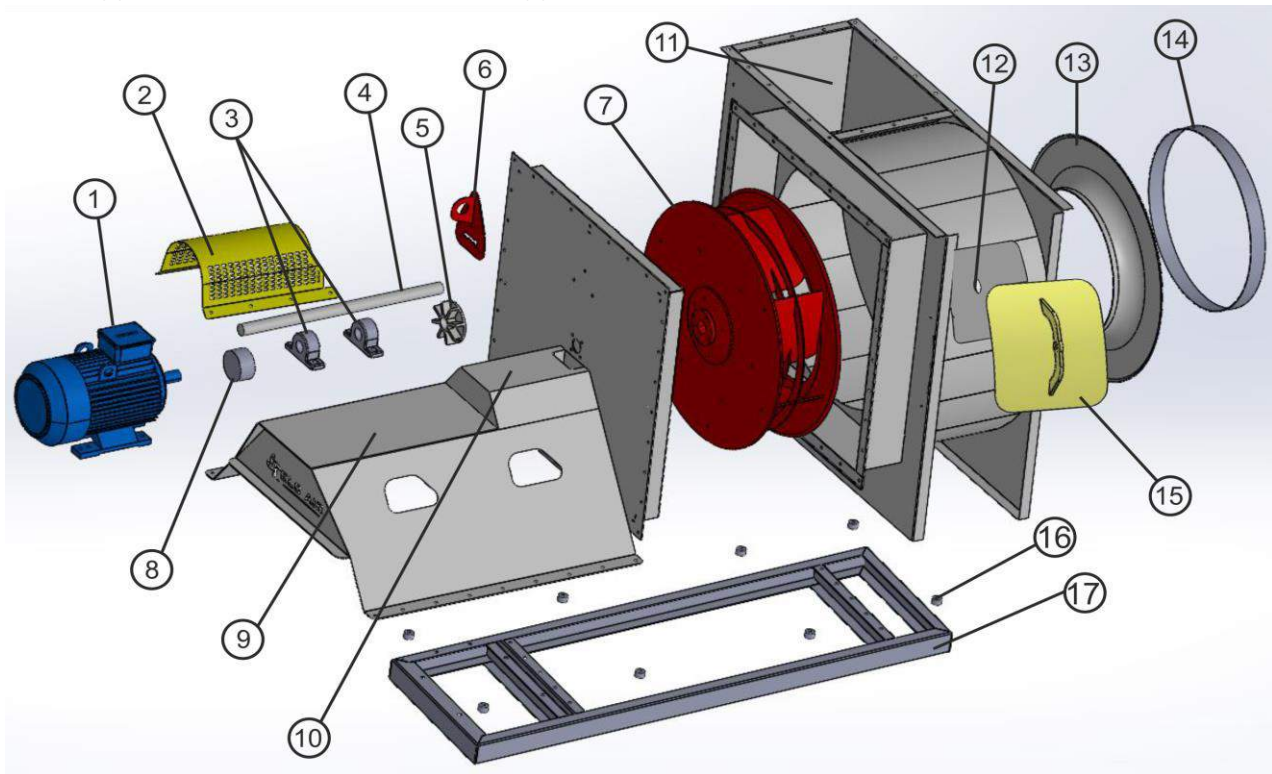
Однозапусковой радиальный вентилятор с муфтой с приводом от вала
